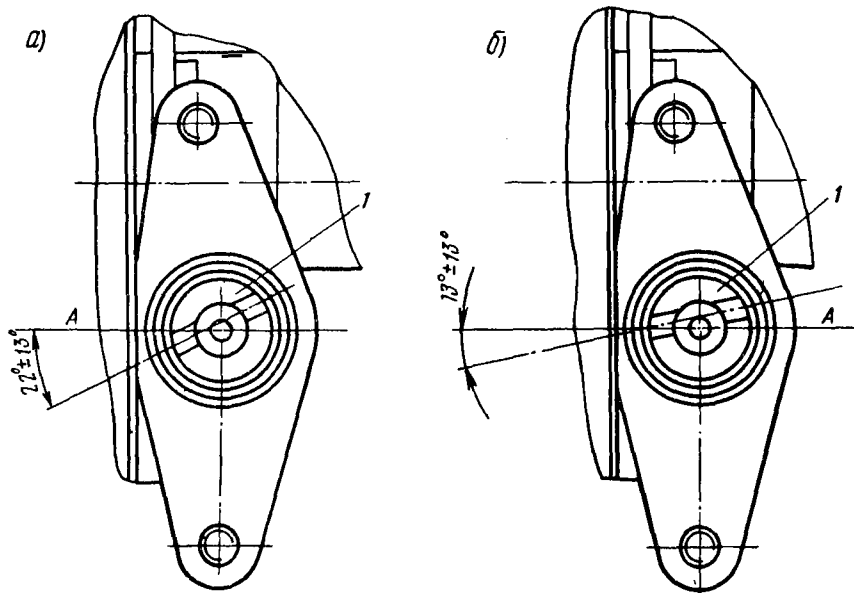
Установка ведомой шестерни привода датчика-распределителя:
